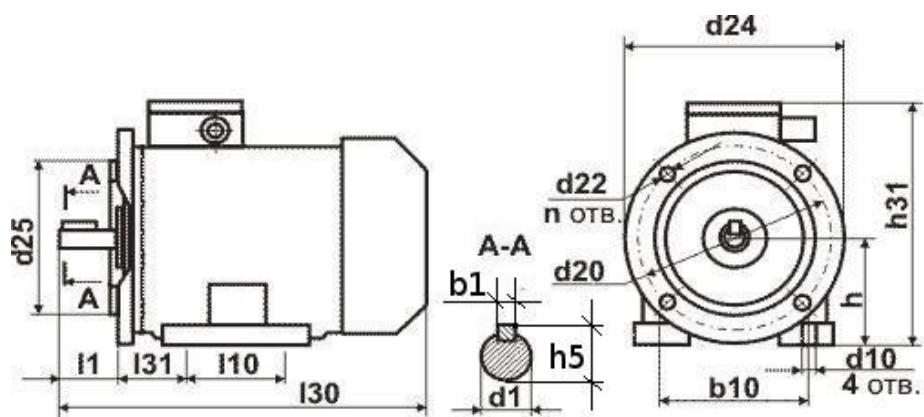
Габаритно-присоединительные размеры двигателей исполнений IM1081, 2081, 3081.
